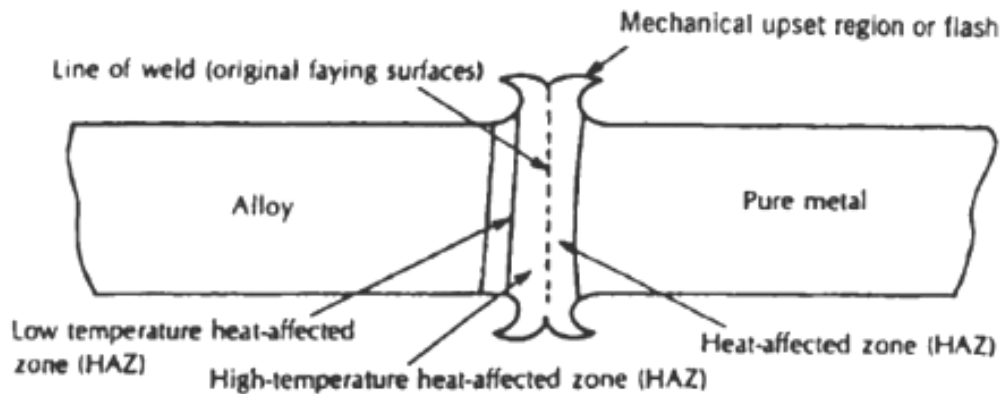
Skema prose pengelasan gesek (*friction welding*)
